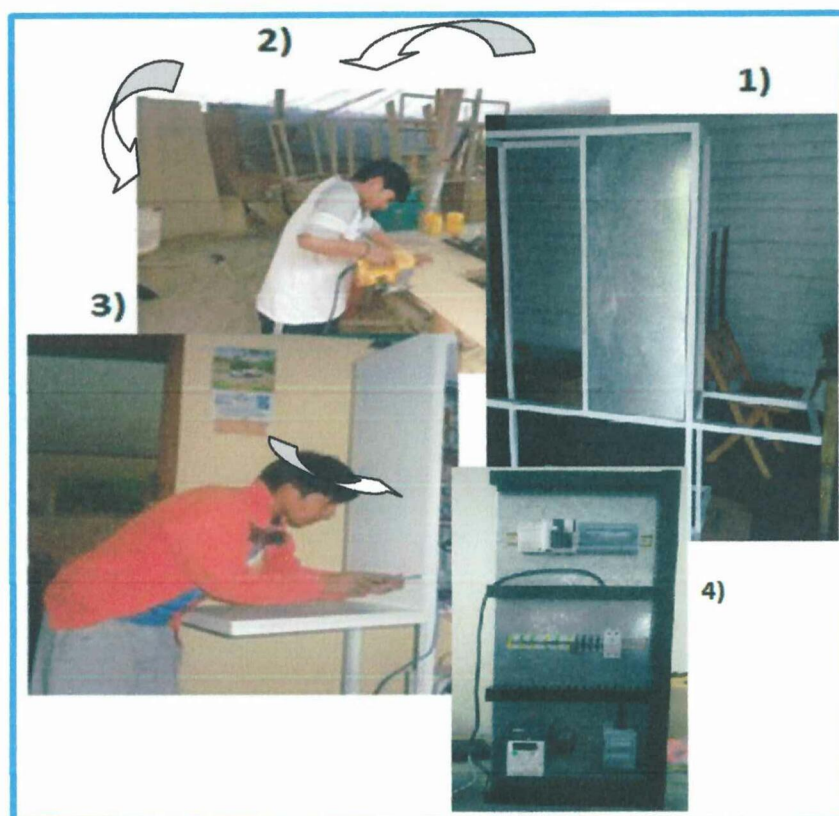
ENSAMBLE DE LA ESTRUCTURA
